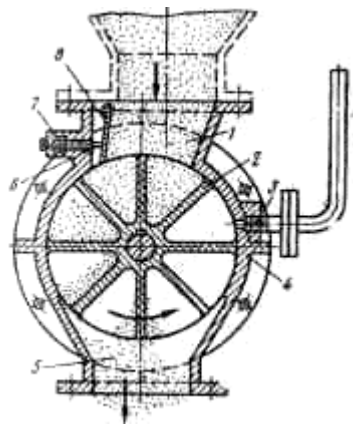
Шлюзовый затвор: 1 — приемная воронка; 2 — вращающийся лопастной барабан; 3 — труба для уравнивания давления в ячейке и приемной воронке; 4 — корпус затвора; 5 — разгрузочная воронка; 6 — штифт; 7 — пружина; 8 — скребок для предотвращения попадания твердых частиц в зазор между лопастью барабана и корпусом.
